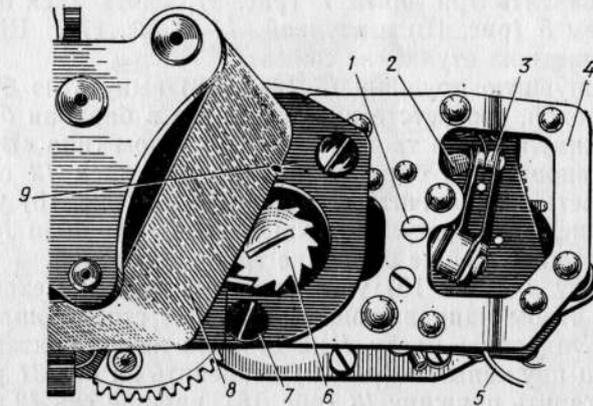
Механизм выдержек на корпусе зеркала с контактами:
